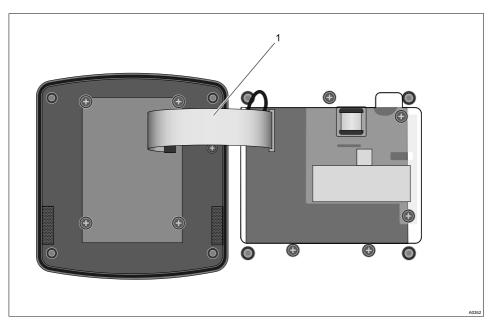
Flachbandkabel in Sockel stecken und verriegeln
